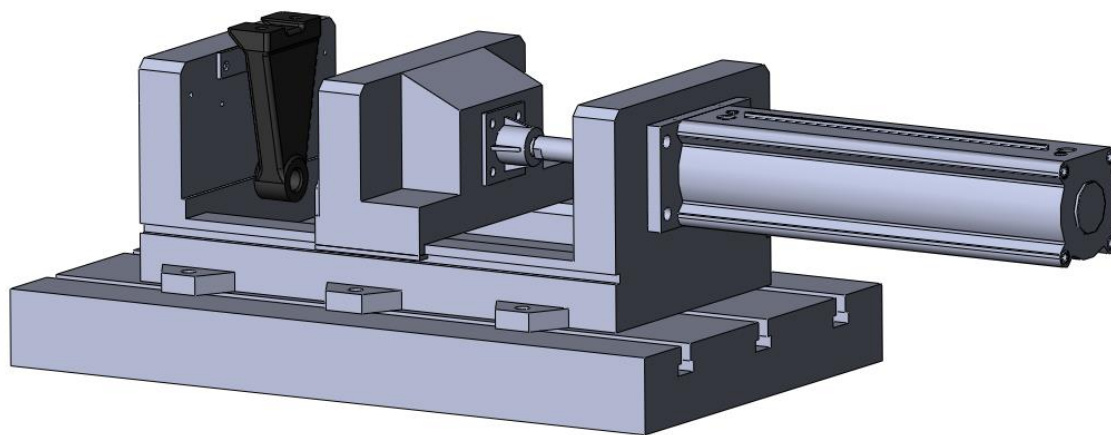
Тривимірна візуалізація заготовки, пневмолещат, фрезерного столу
